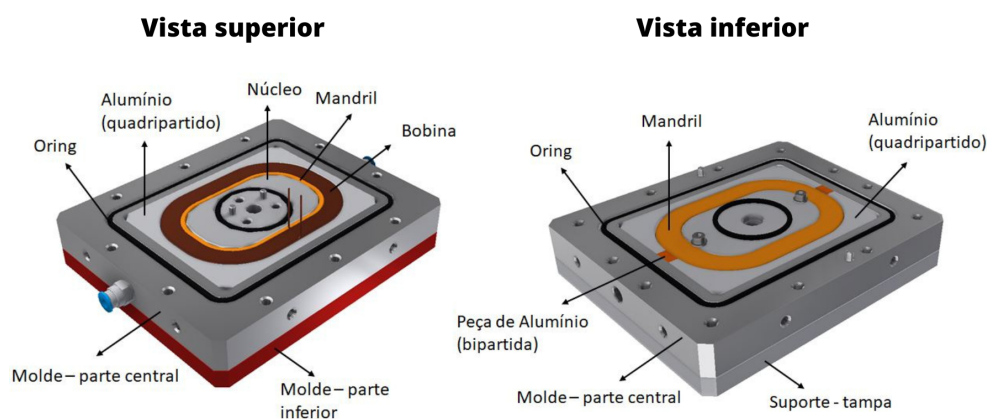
Representação do desenho técnico do conjunto para impregnação à vácuo: vista superior e inferior. Fonte: adaptado de [19]
